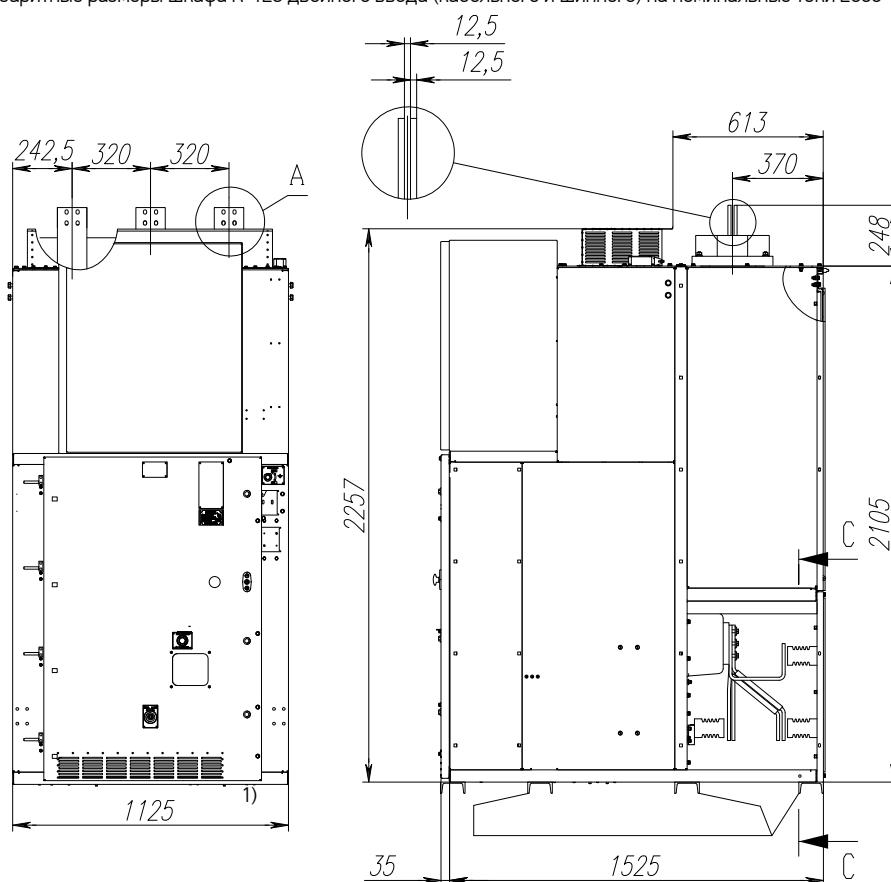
Общий вид и габаритные размеры шкафа К-128 двойного ввода (кабельного и шинного) на номинальные токи 2000-4000 А
